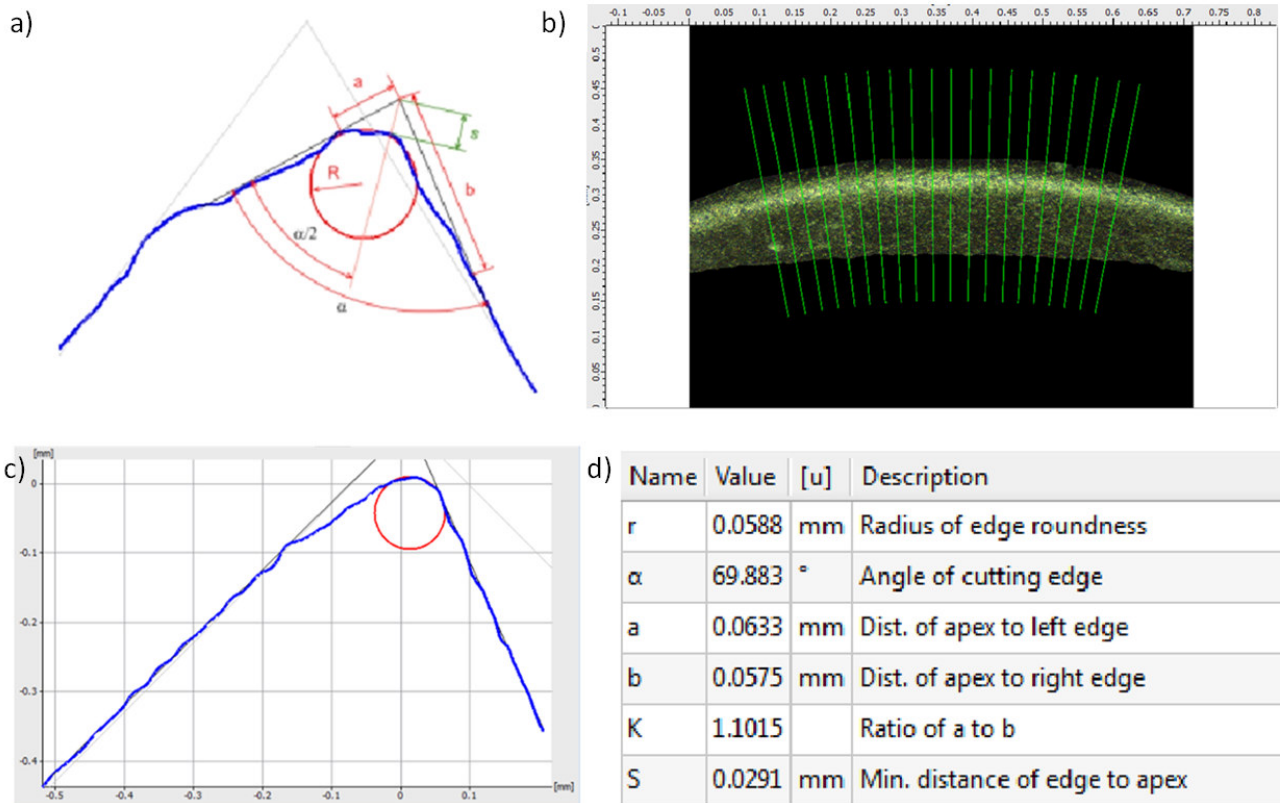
Pomiar profilu konstrukcyjnego elementu zwijacza wióra
